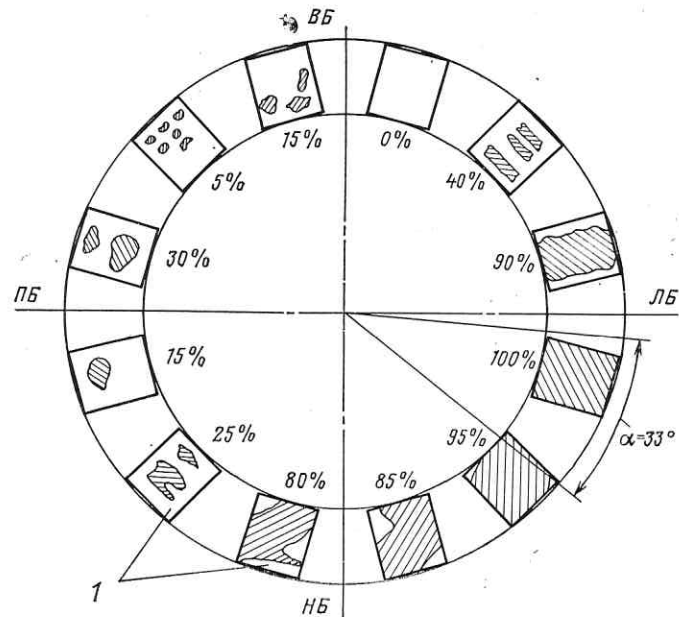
Эскиз повреждения направляющего подшипника гидрогенератора типа СВ-1340/150-96:
